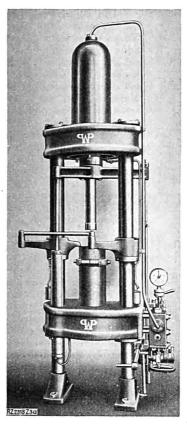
Kopierminenpresse mit selbsttätiger Steuerung von Werner & Pfleiderer, Kannstatt
